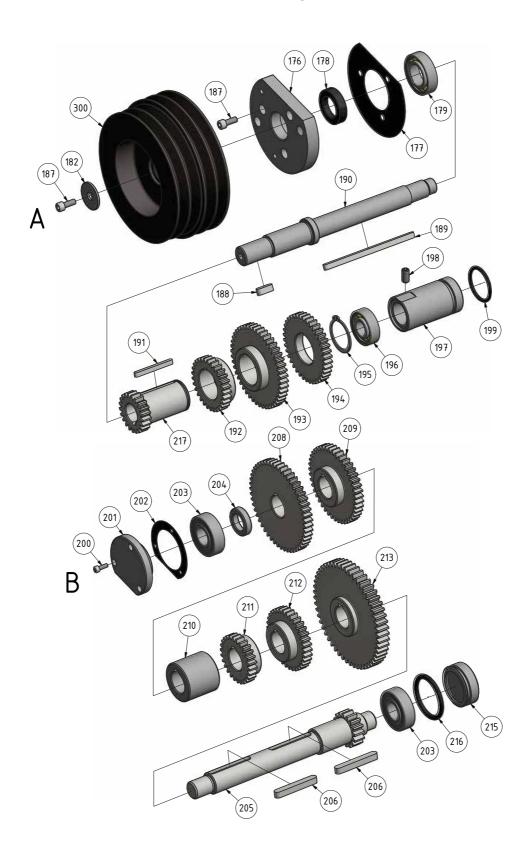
Getriebe Spindelstock 3-6 - Headstock gear 3-6
